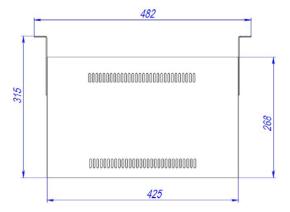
Внешний вид и габаритные размеры исполнения SGS-16FO-H
